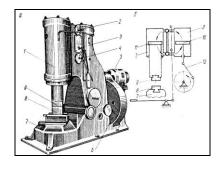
Пневматический молот: а) общий вид; б) кинематическая схема.
